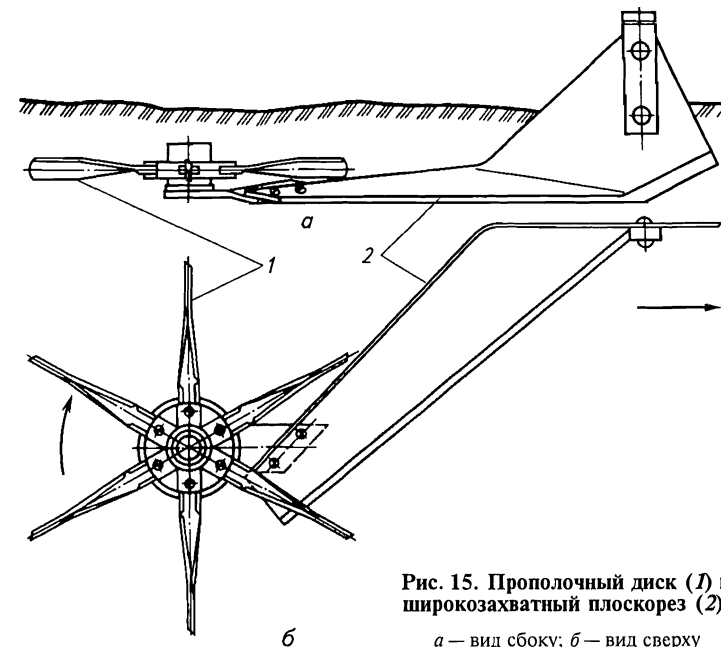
Прополочный диск (1) и широкозахватный плоскорез (2):
